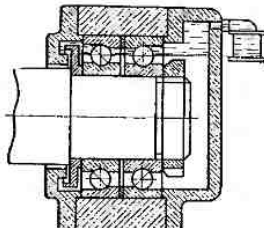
Смазочное отверстие в крышке корпуса подшипника
